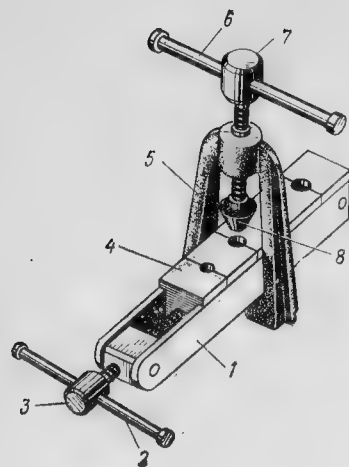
1 — колодка; 2 — ручка; 3 — винт сжима вкладышей; 4 — вкладыши; 5 — разбортовка; 6 — вороток; 7 — винт силовой; 8 — конус
